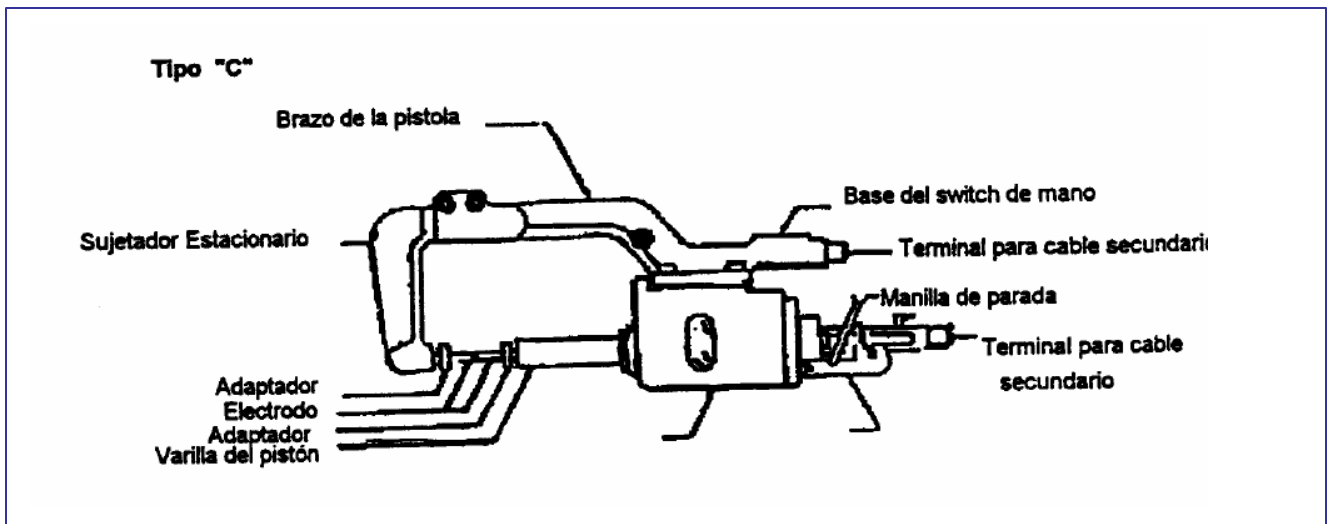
Pistola de soldadura por electropunto tipo "C"
